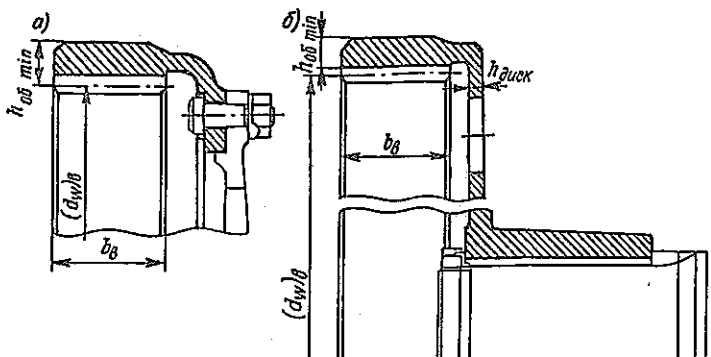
Неплавающие вращающиеся центральные колеса с внутренними зубьями
